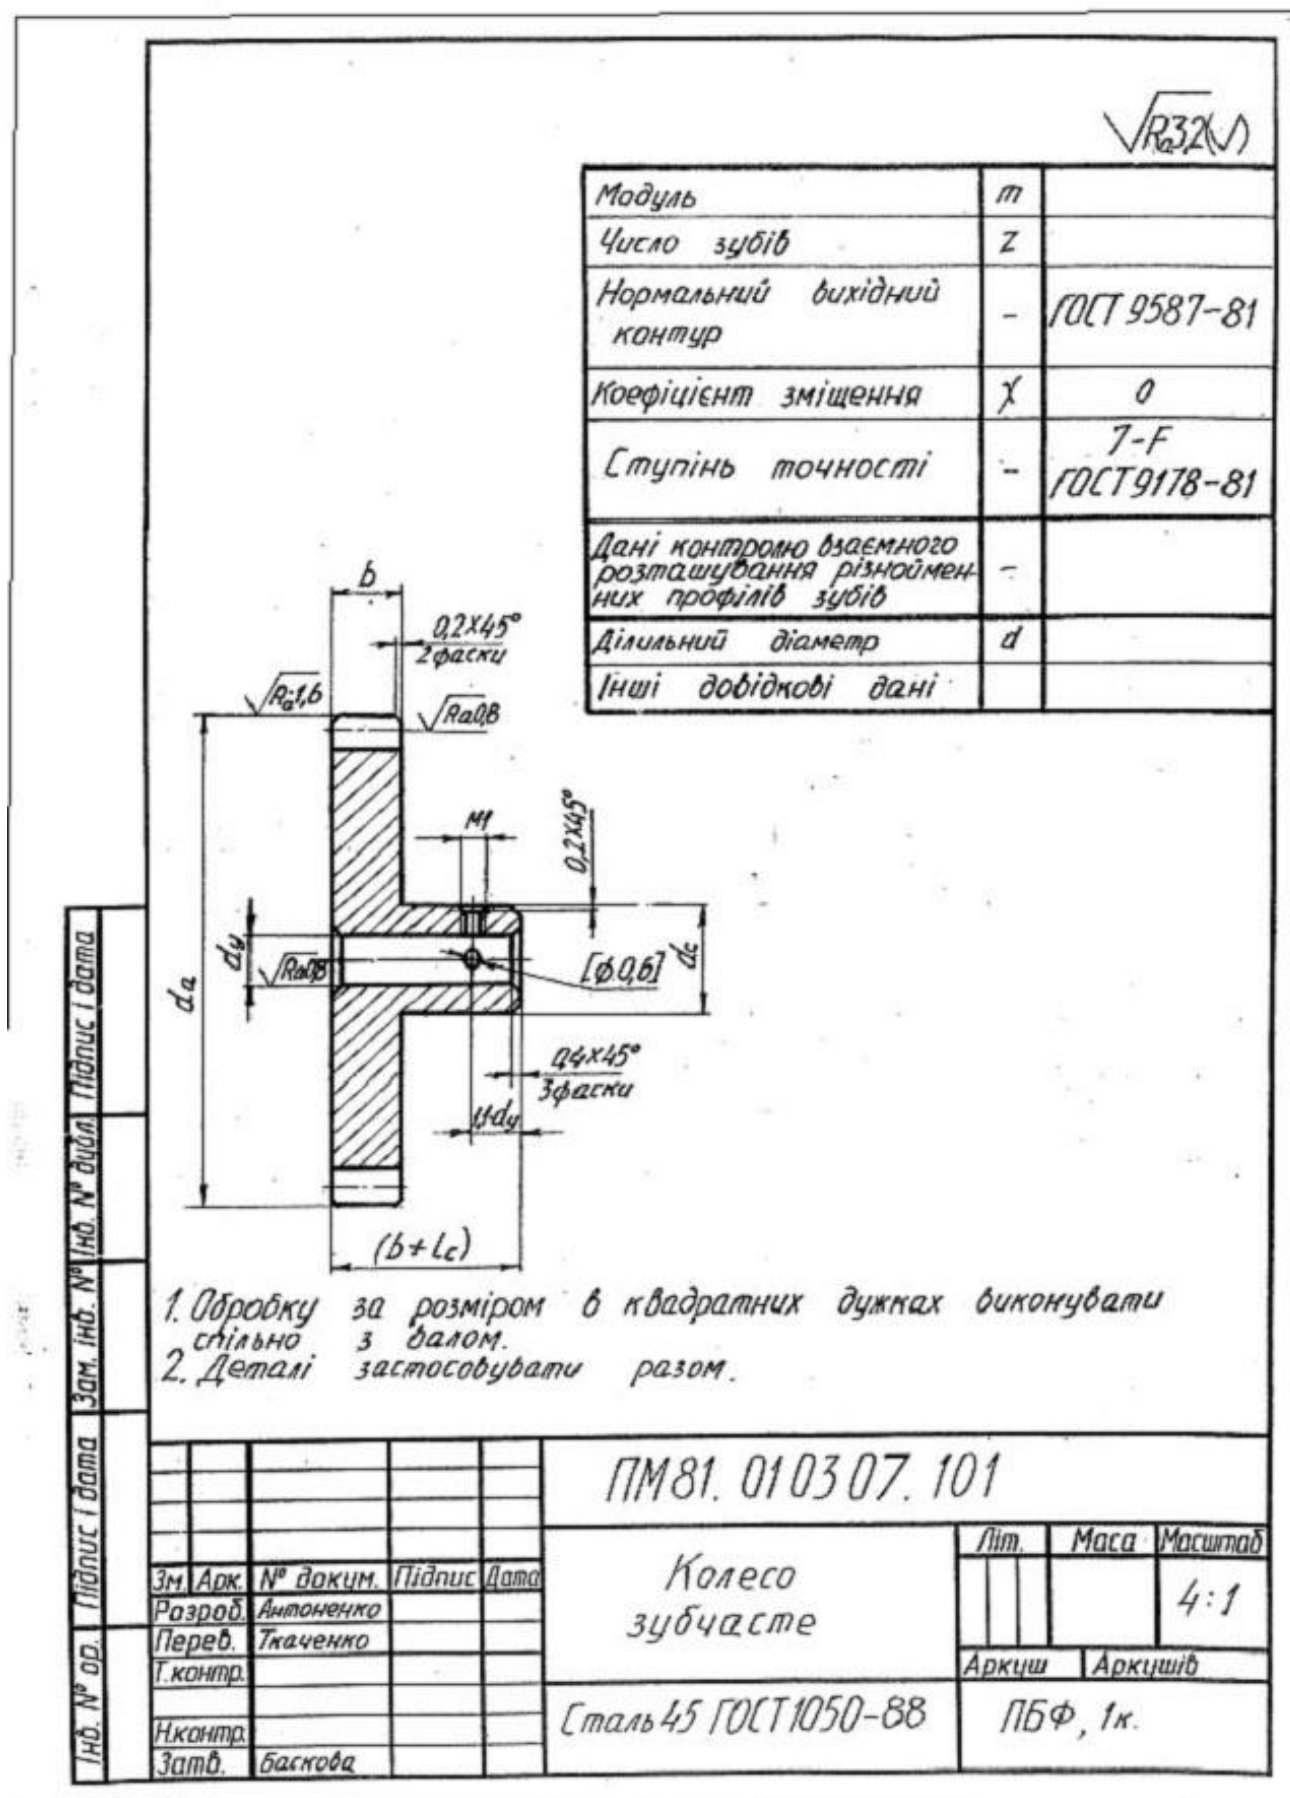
Кресленник циліндричного зубчастого колеса
